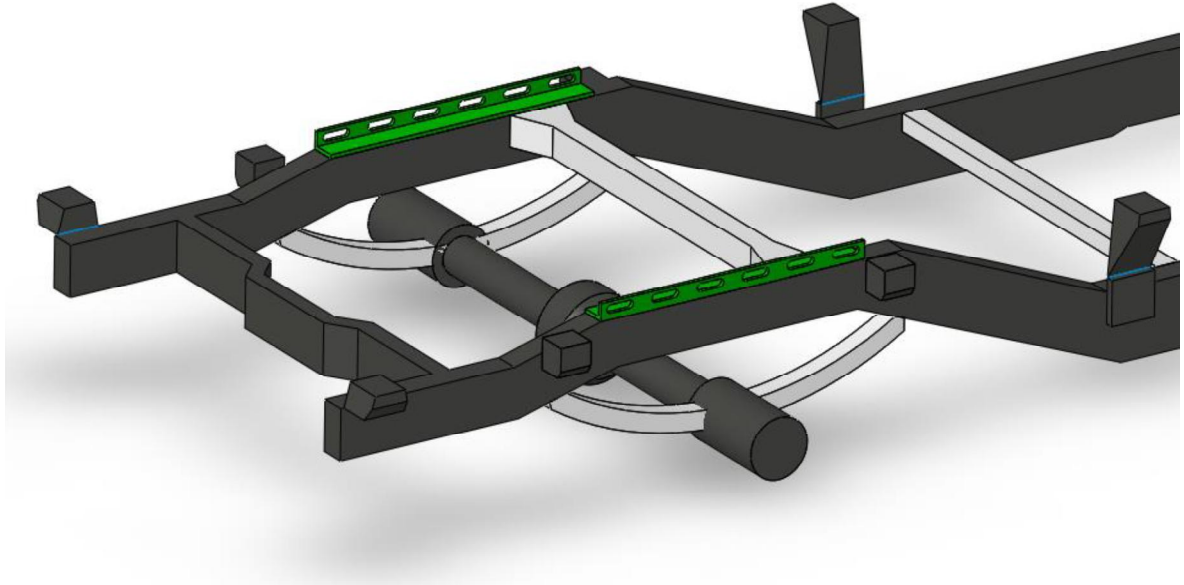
Angulares soldados a la estructura del chasis (Fuente: SolidWorks)
